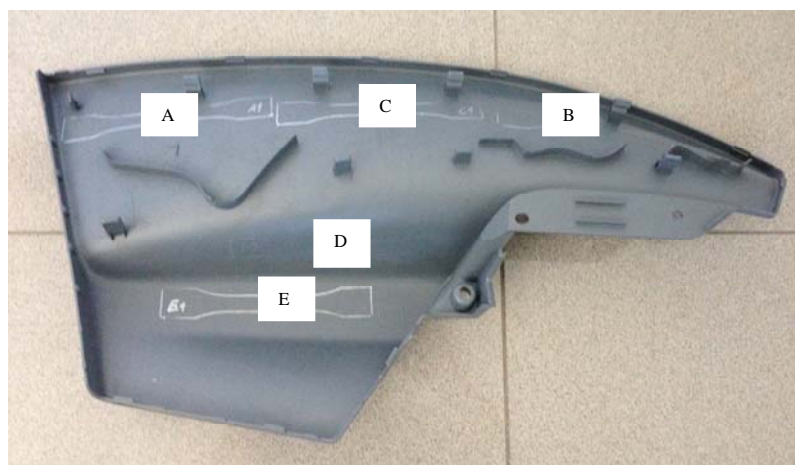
Áreas de extracción de planchas para ensayo. Inserto
